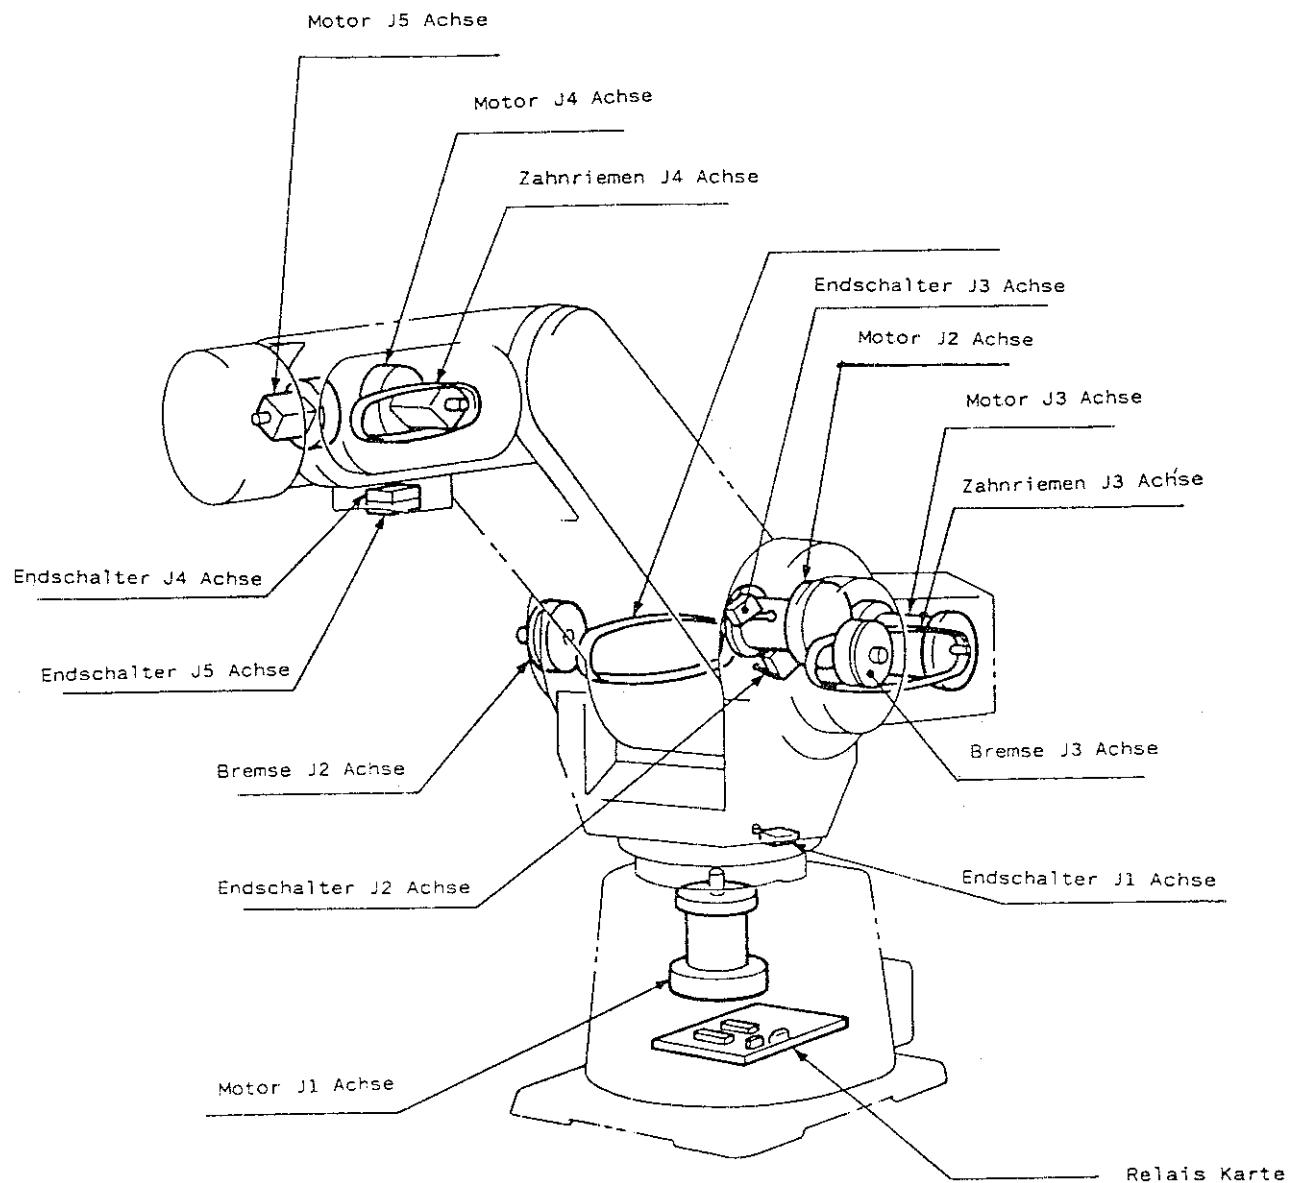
Bezeichnungen (Innenansicht)
